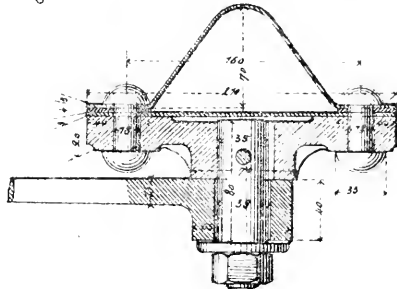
Elevation du poteau de manoeuvre à 0,04 p^r 1^m
